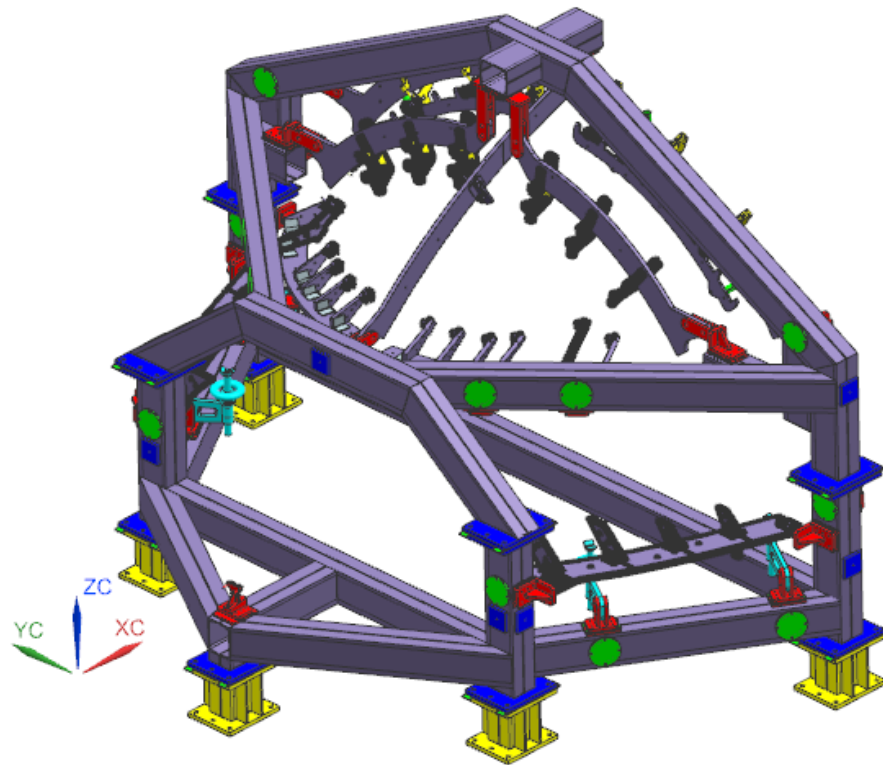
Итоговый вид сборочного приспособления.
